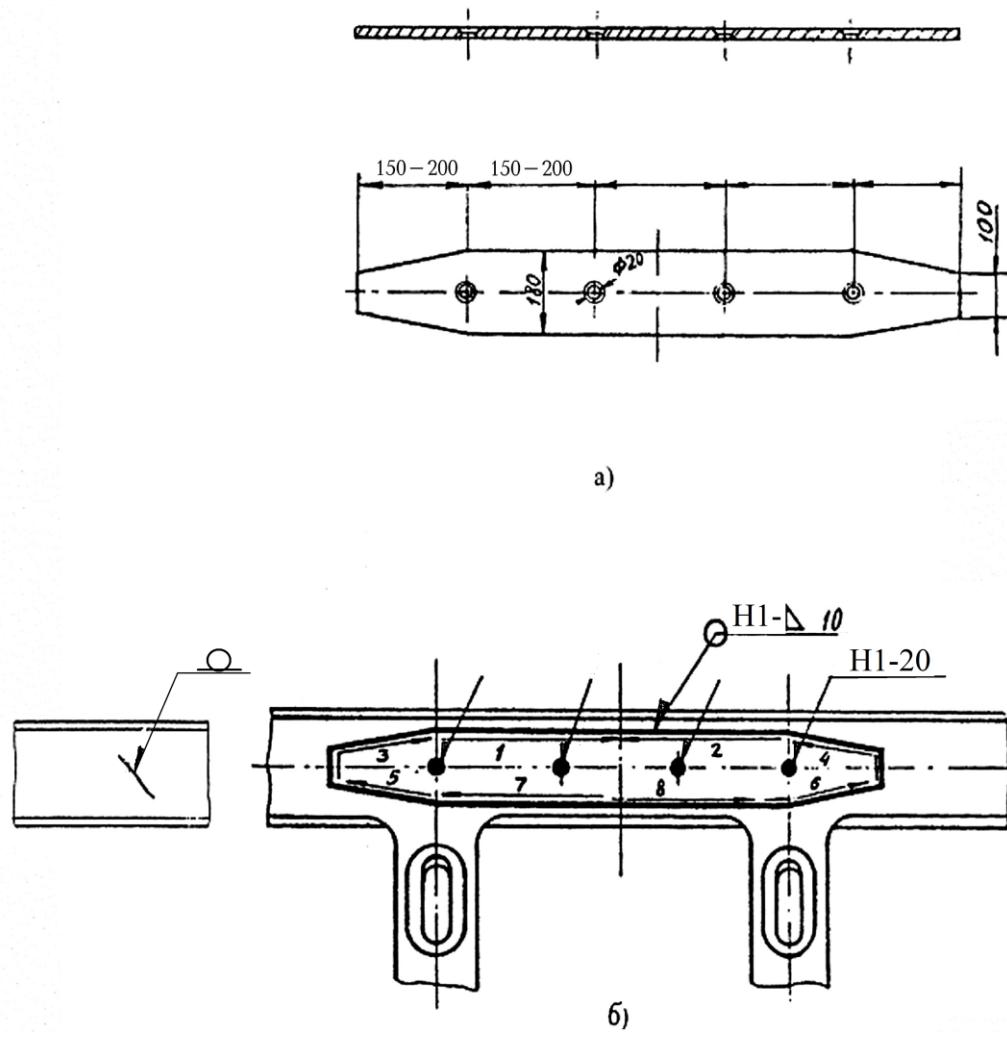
Основные дефекты рамы тележки типа ЦМВ, ремонтируемые сваркой или наплавкой
